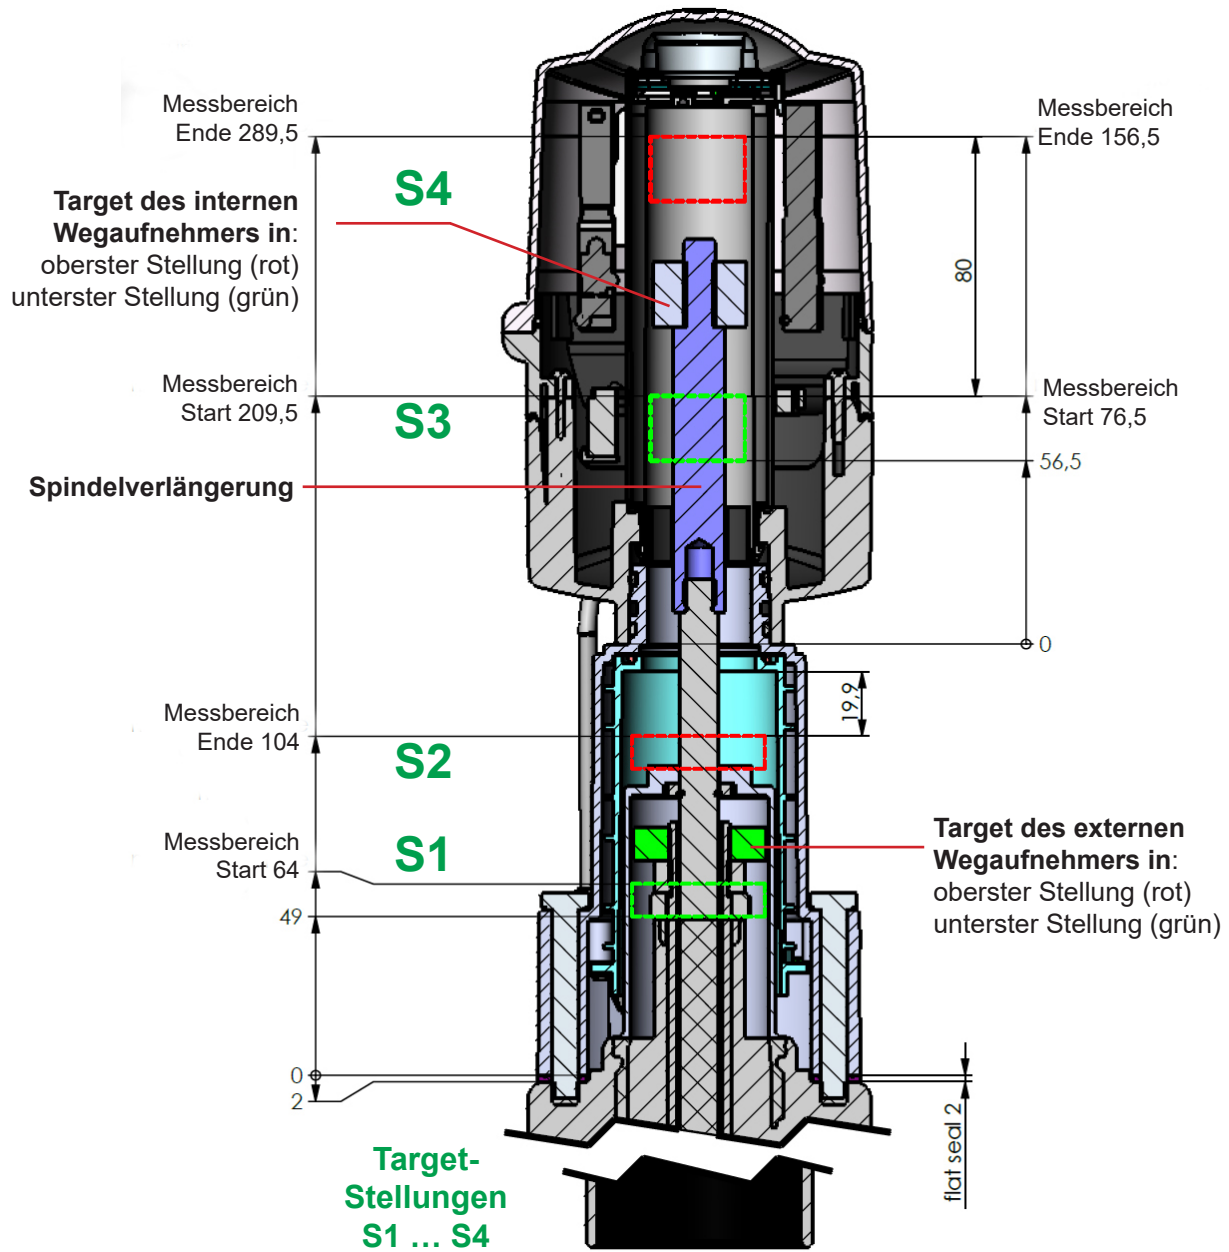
Schnittansicht von Gerät und Spindel mit beiden Targets des internen und externen Wegaufnehmers
